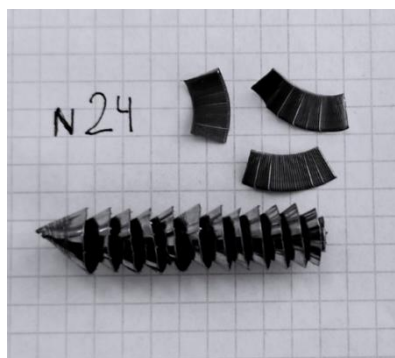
Стружка, полученная при сверлении заготовки № 24
